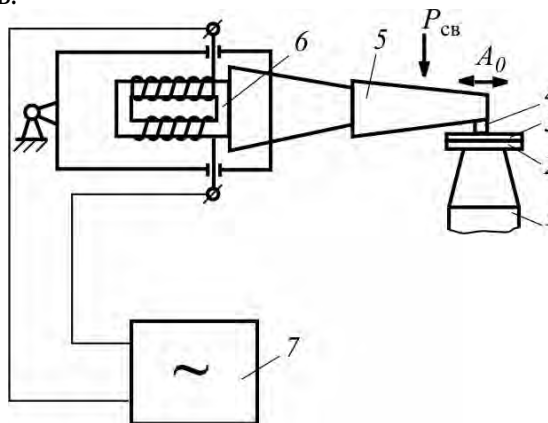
Схема установки для ультразвуковой сварки с продольными колебаниями:
